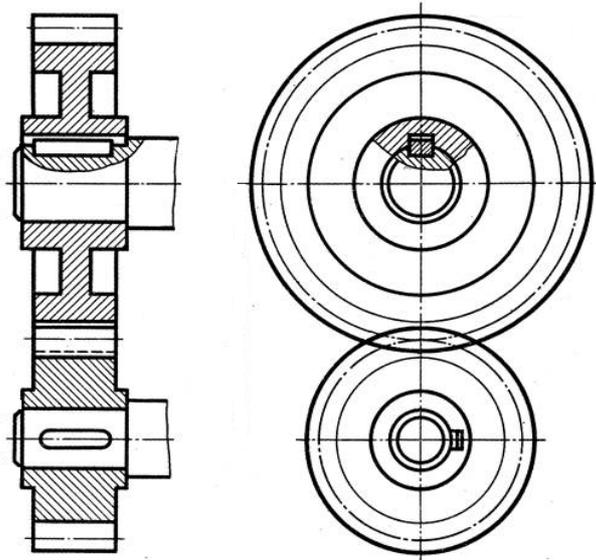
Изображение цилиндрической передачи на сборочных чертежах
